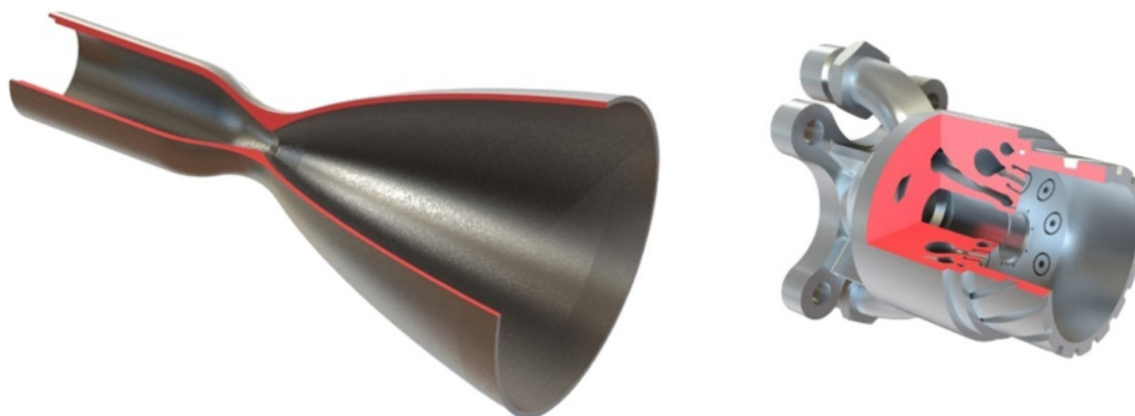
3D-модели корпуса камеры и смесительной головки
